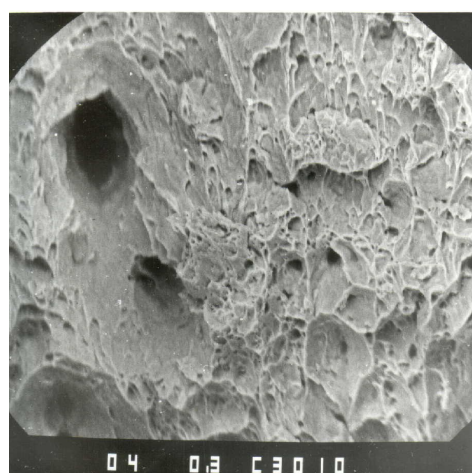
Образец после испытаний на ударный изгиб. Общий вид поверхности ямки; × 300
